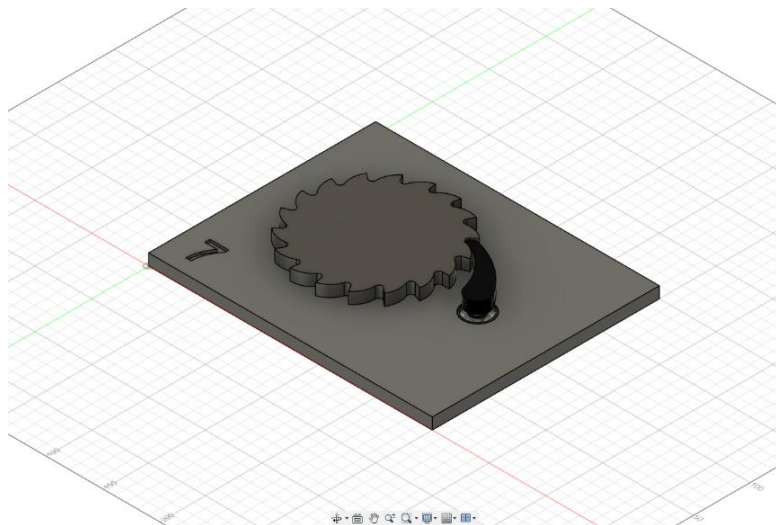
Τρισδιάστατη απεικόνιση βάσης συγκράτησης
